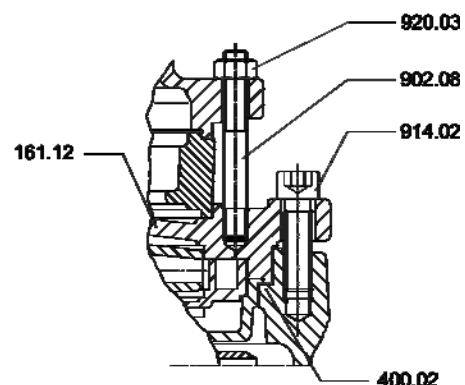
Исполнение крышки корпуса при типоразмерах 2/40-250/01 и 2/50-250/01
